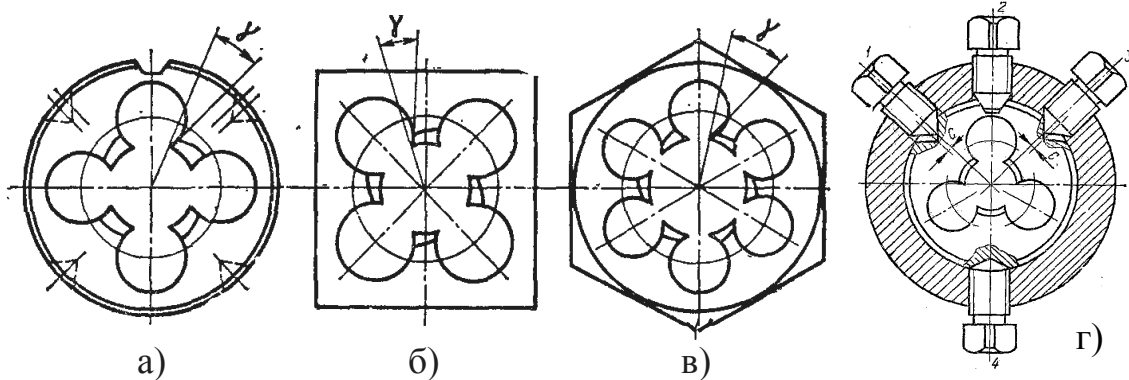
Виды плашек: а) – круглые, б) – квадратные, в) – шестигранные, г) – схема закрепления плашек.
